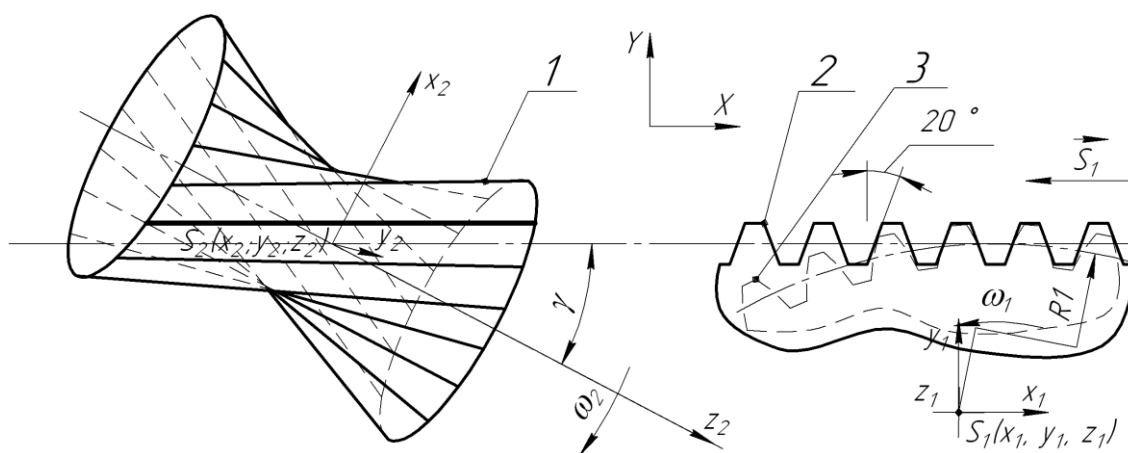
Схема формообразования гиперboloидной винтовой поверхности:
